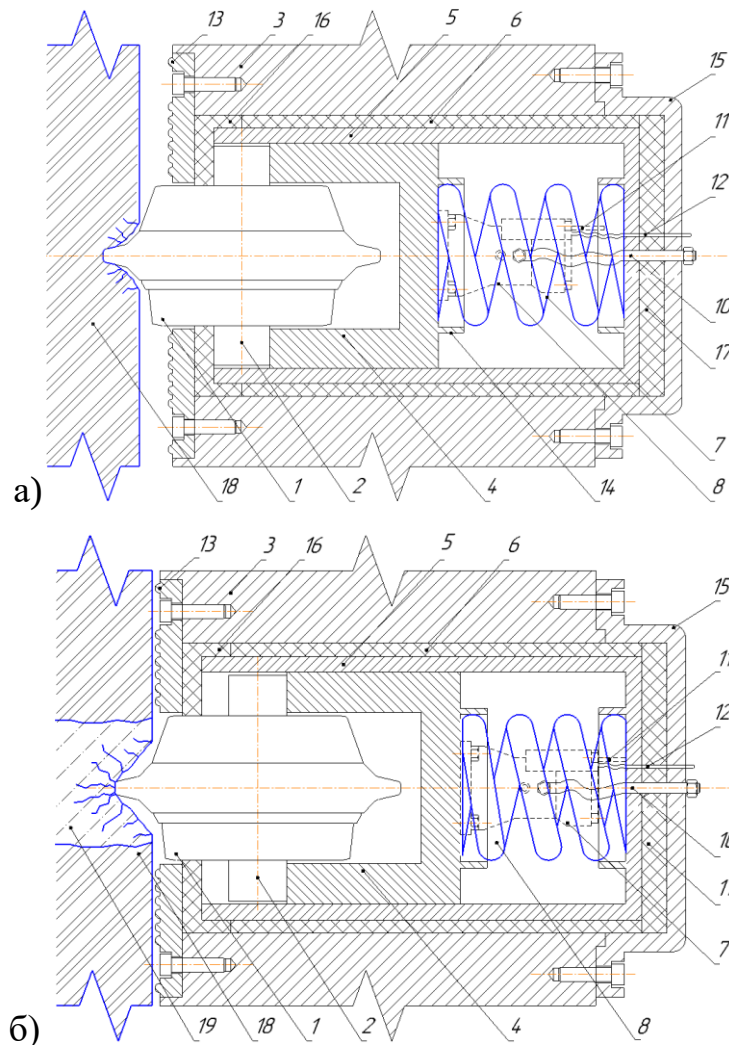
Разрушение виброактивной шарошкой: а – кембрийской глины; б – прослойки известняка
